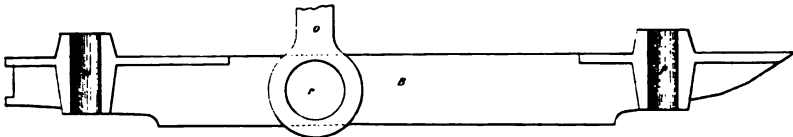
Coupe du plancher inférieur du cadre n° II.
